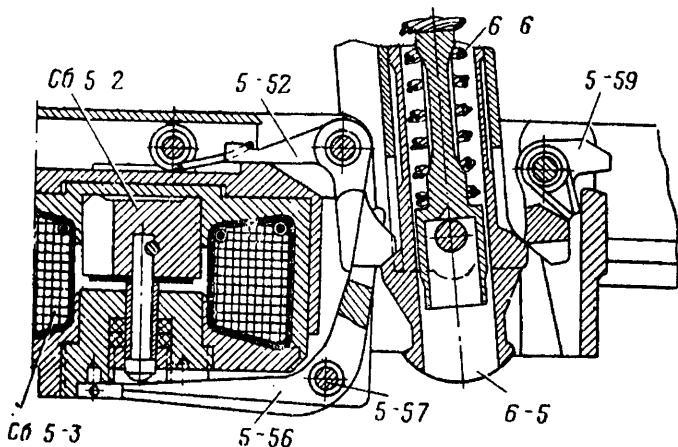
Положение деталей электроспуска перед выстрелом (обозначения деталей см. в приложении I)
